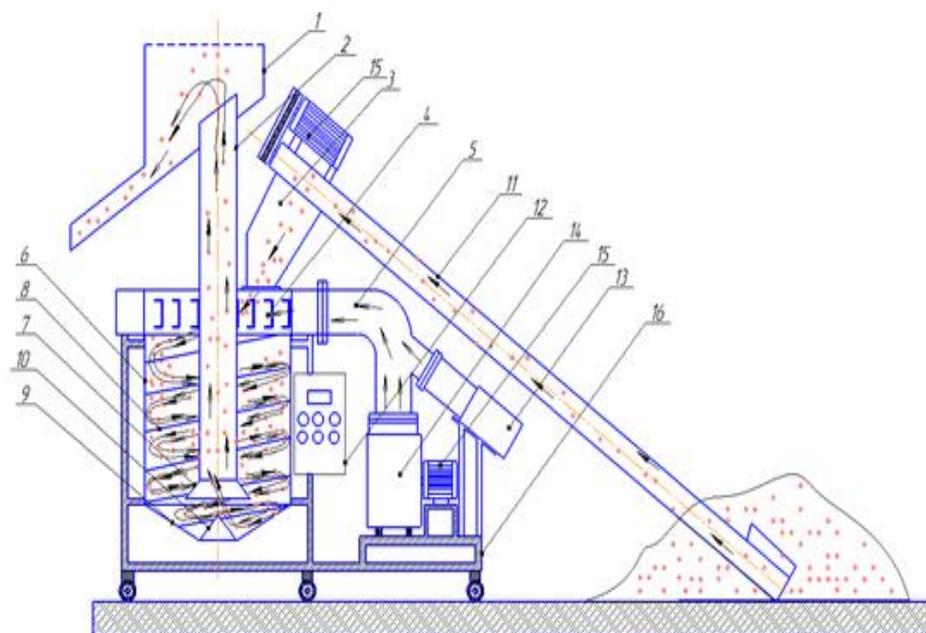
Вихревая газопламенная сушилка ВГС-1Д
